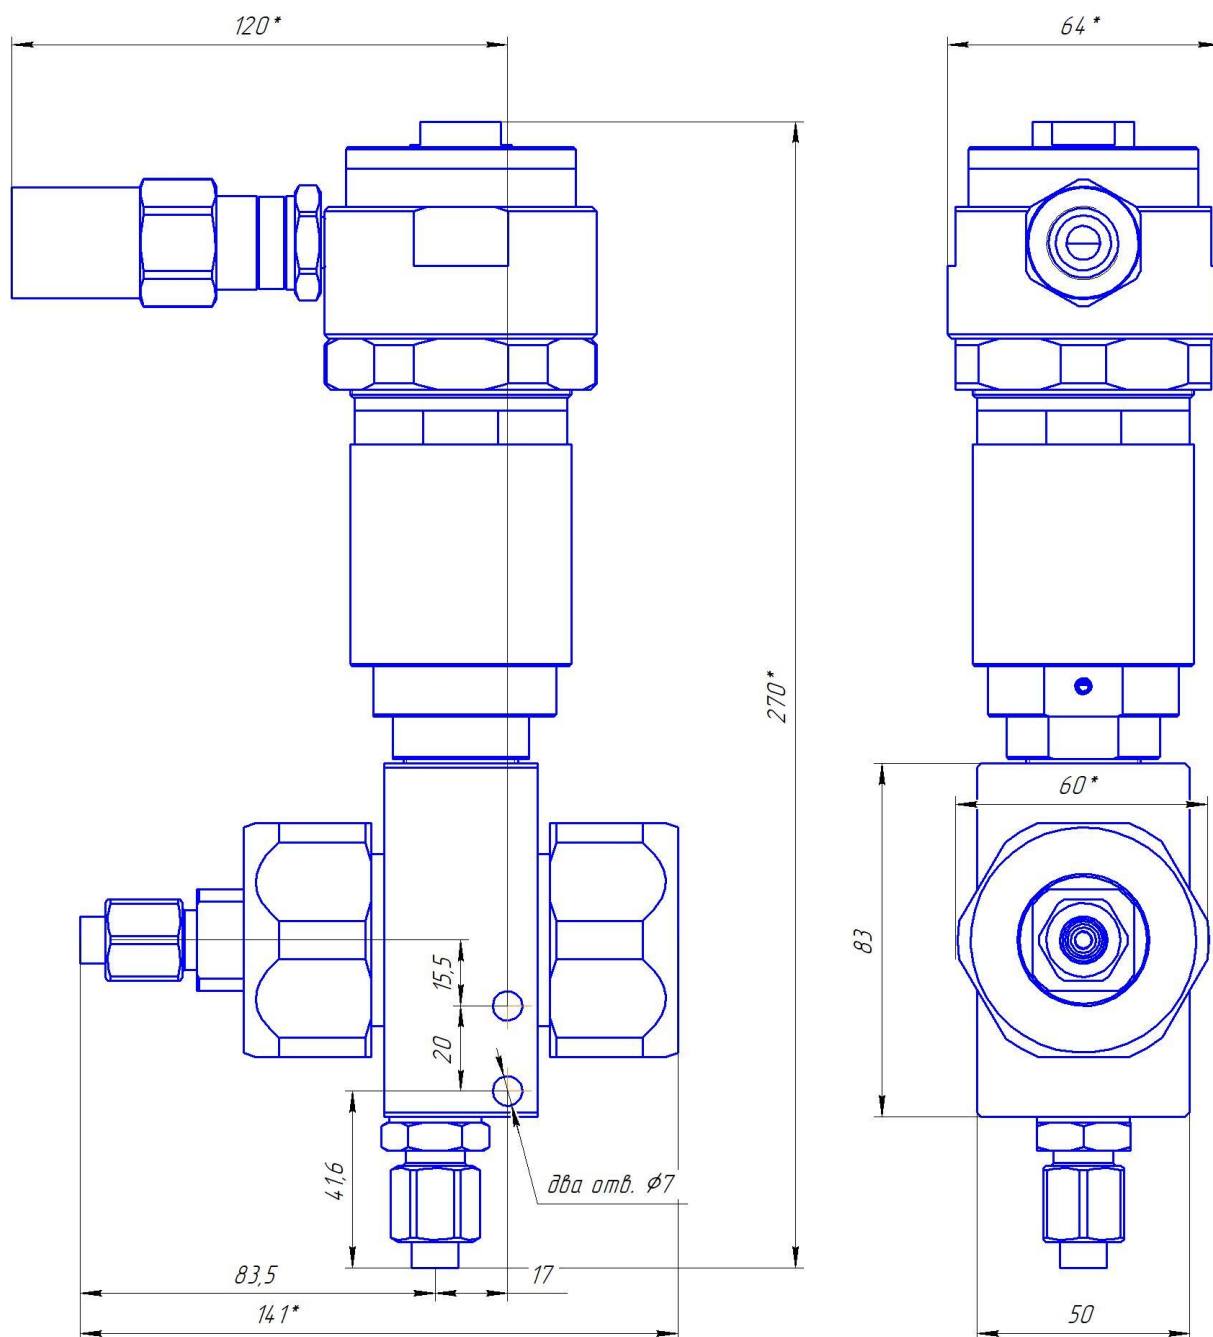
Габаритные и установочные размеры исполнений клапана КРВ-М-2/2-ВД, КРВ-М-3/2- тс кабельным вводом для монтажа кабеля в металлорукаве РЗ-ЦХ-15
